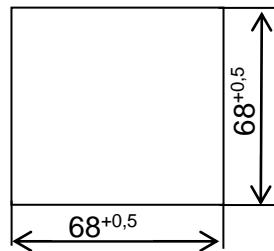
Габаритные размеры устройств 72x72x85 mm
